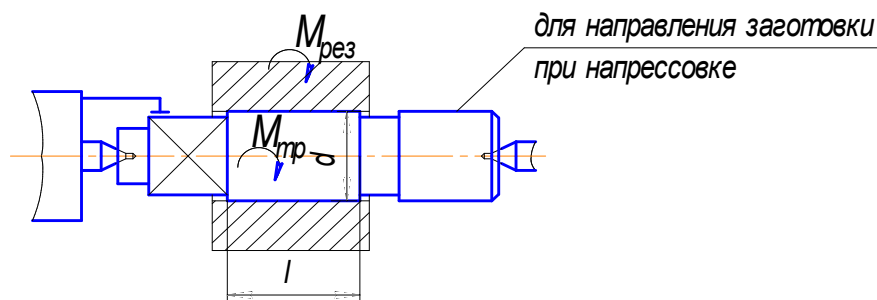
Схема цилиндрической оправки для посадки заготовок с натягом
